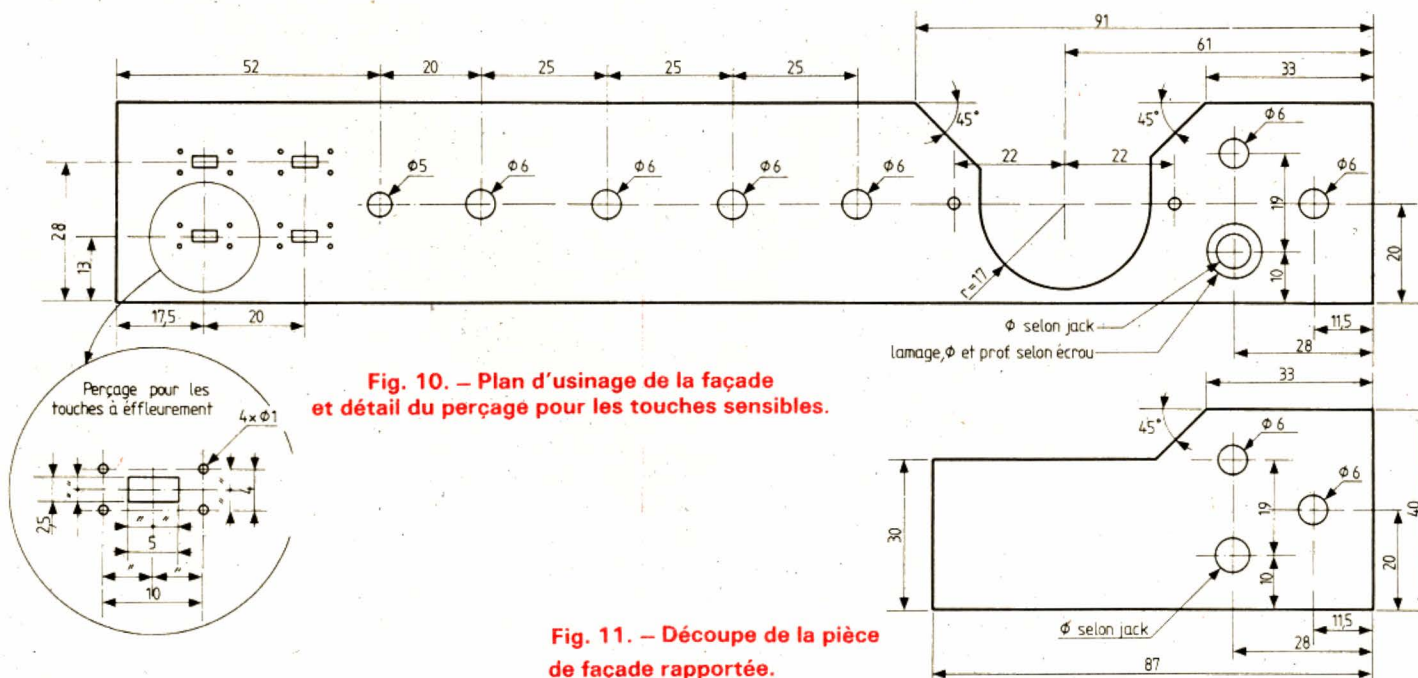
Plan d'usinage de la façade et détail du perçage pour les touches sensibles.
